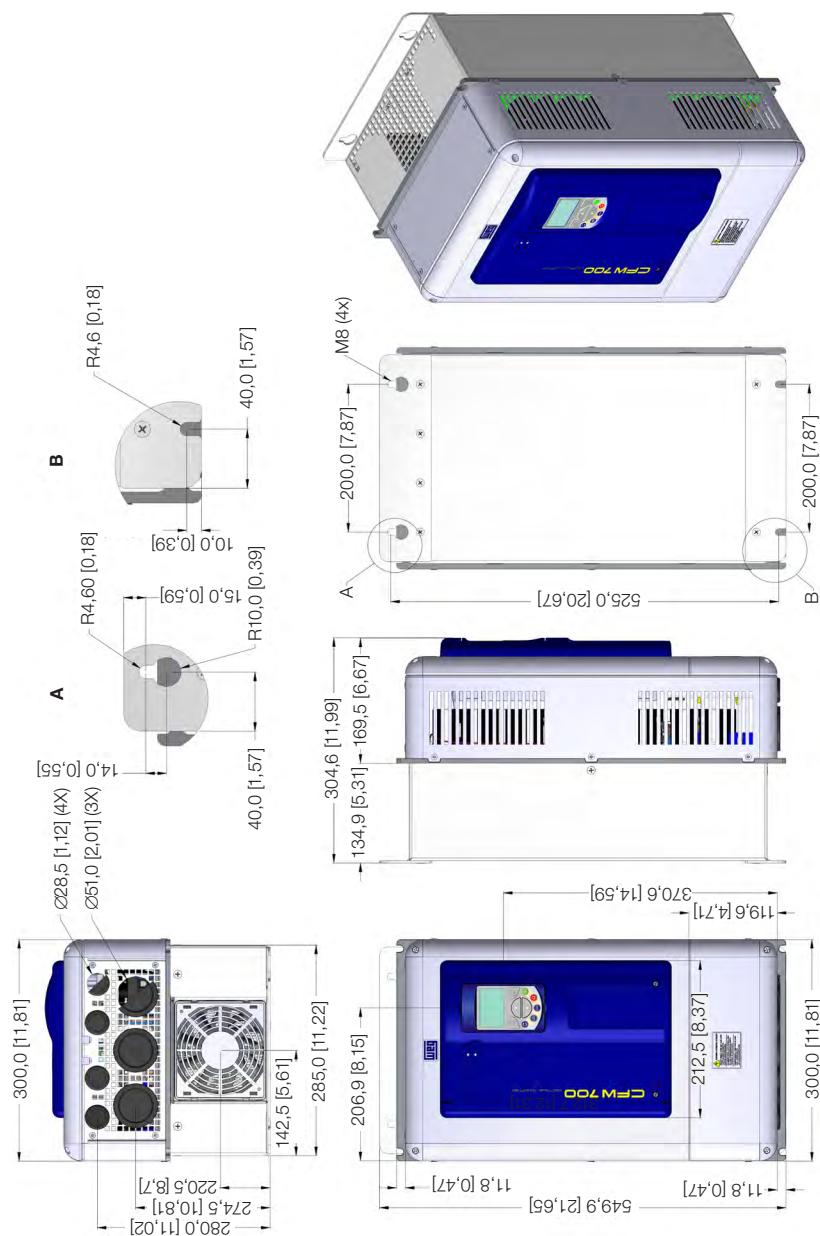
Umrichterbaugröße in mm [in] - gehäuse D
